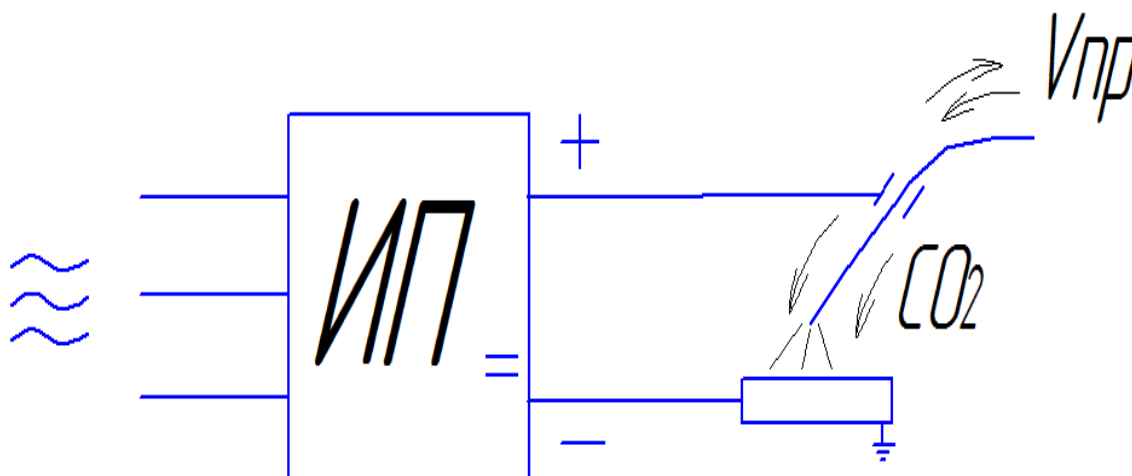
Схема включения сварочного выпрямителя
